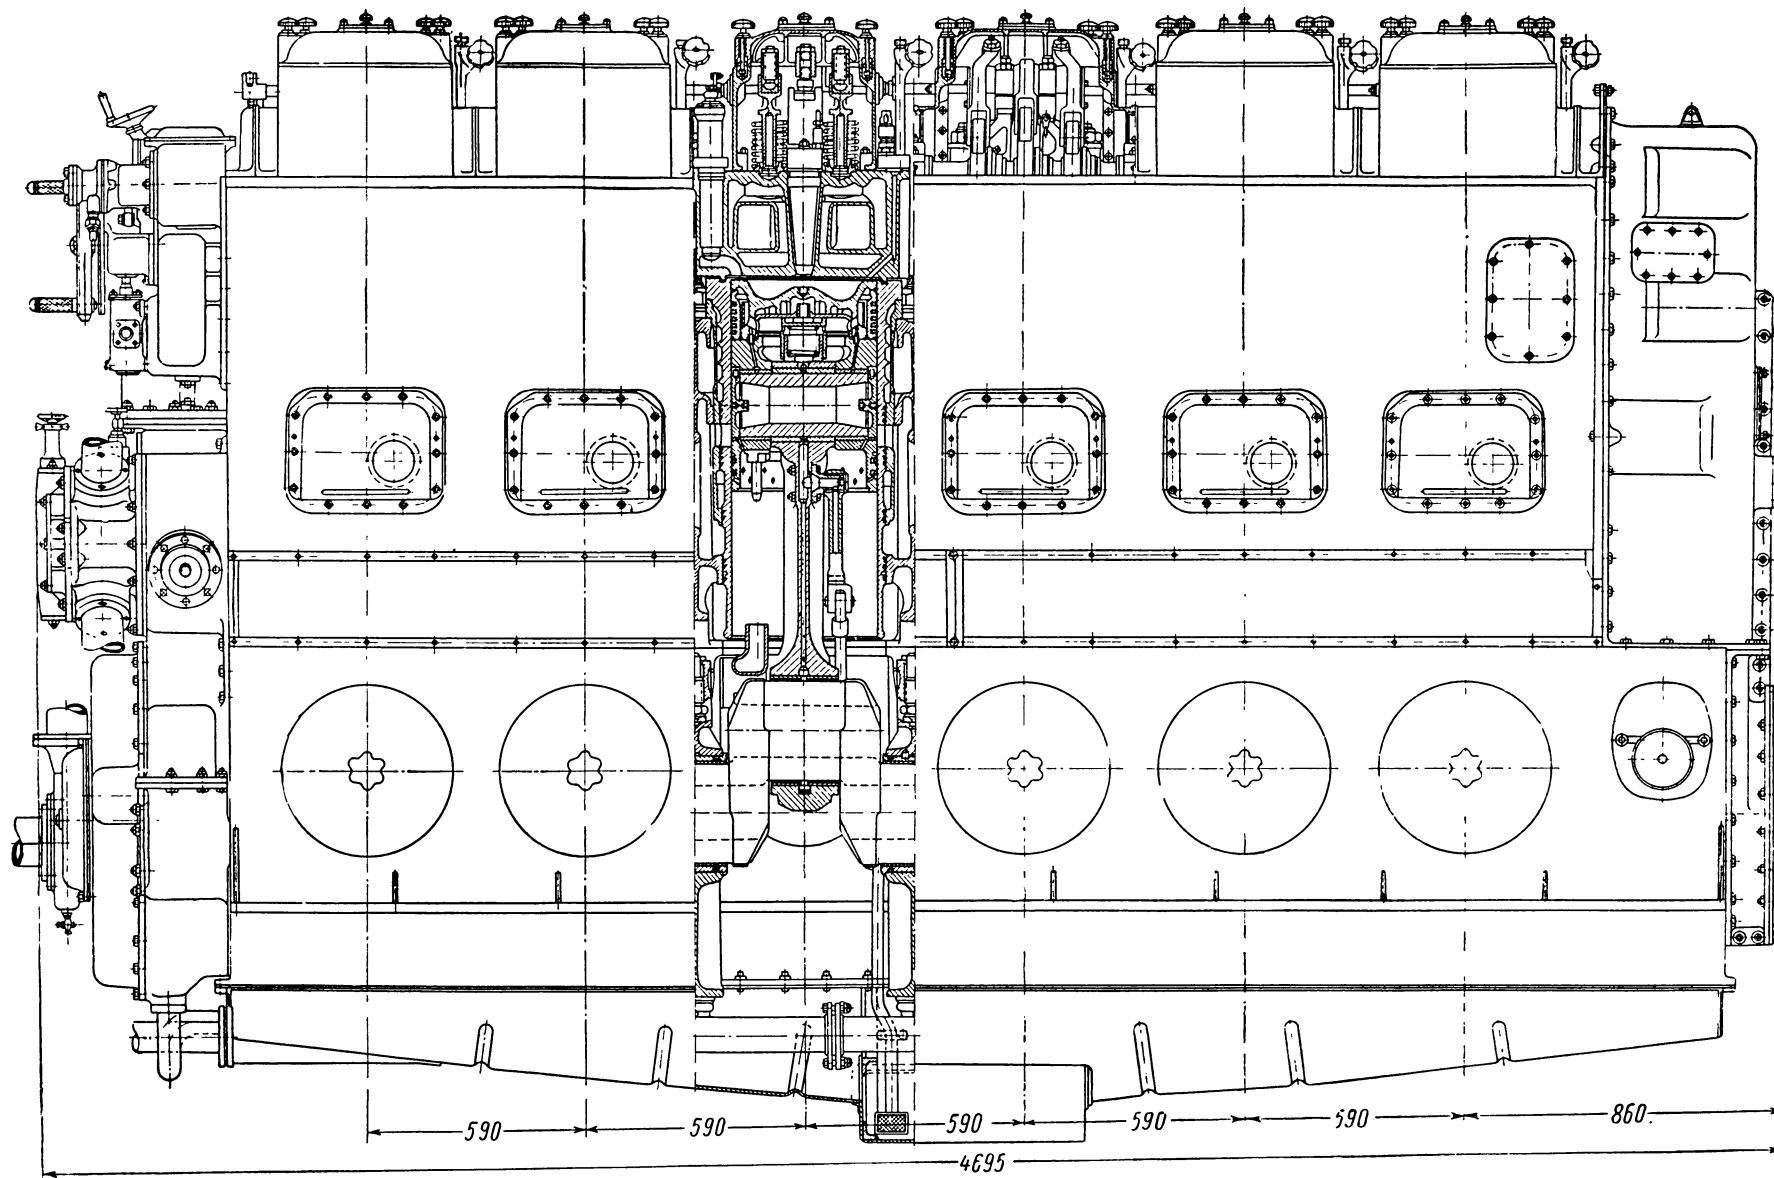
Общий вид двигателя со стороны распределительного вала и продольный разрез одного цилиндра.
